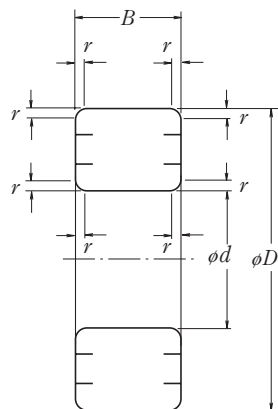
Габаритные размеры радиальных шарикоподшипников и роликоподшипников
